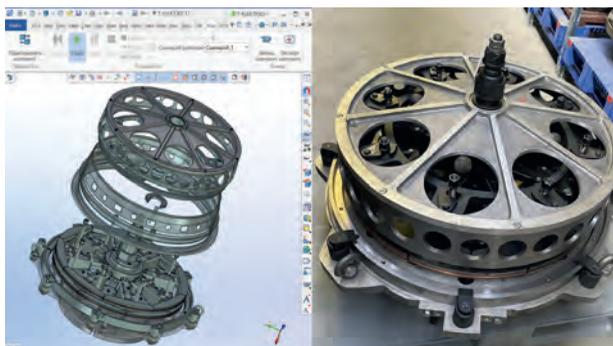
Номинация «Эксперт». Сварочное приспособление
